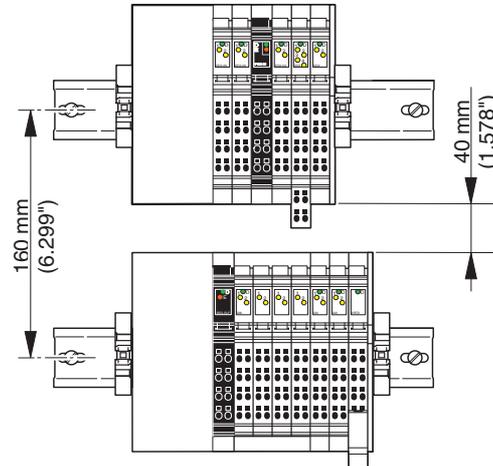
Montageabstände bei Montage außerhalb eines Klemmenkastens
